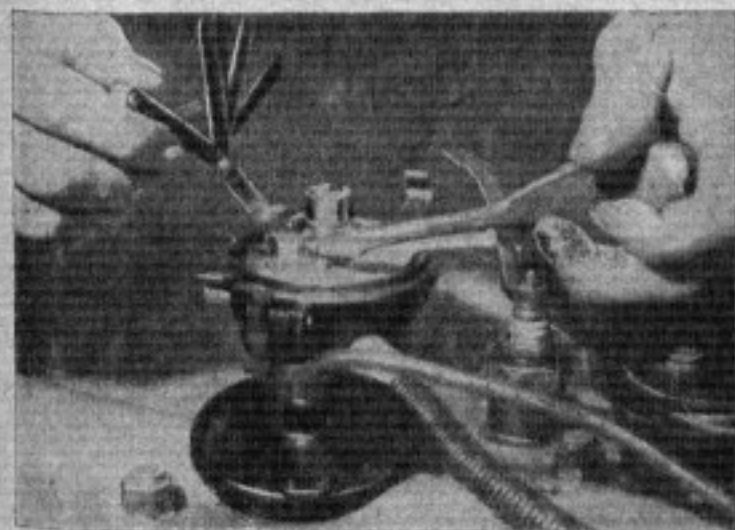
Регулировка зазора между контактами прерывателя (на двигателе ГАЗ-А)
